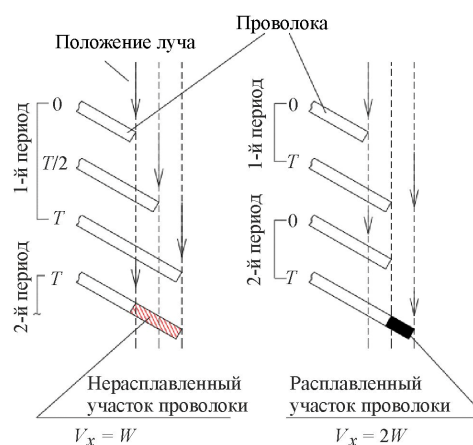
Схема выбора скорости движения луча вдоль развертки
